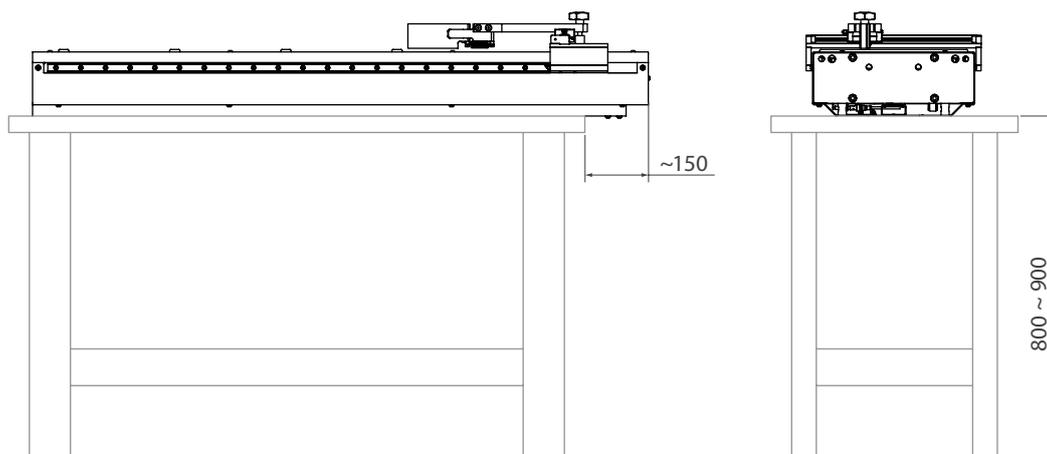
Position du bâti principal sur un banc de travail ou un plan haut
